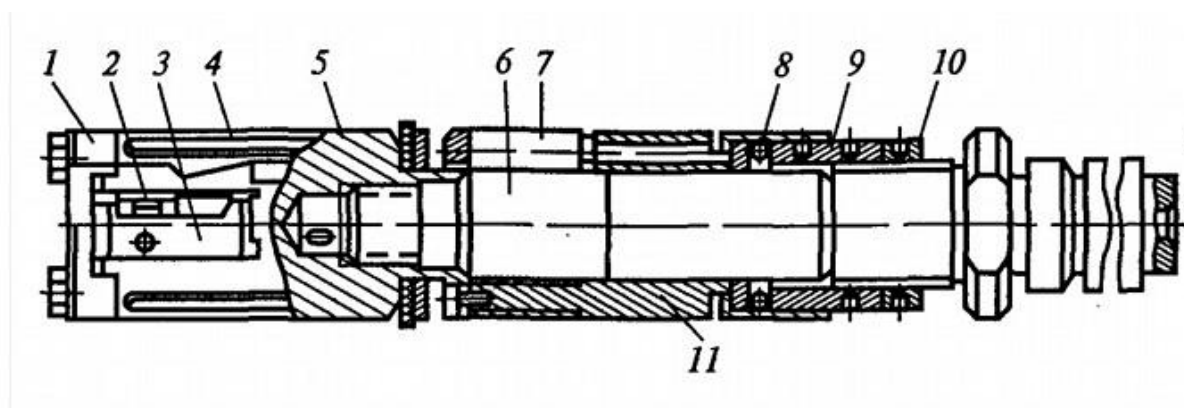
Комбинированный инструмент для растачивания и раскатывания стальных гидроцилиндров:
